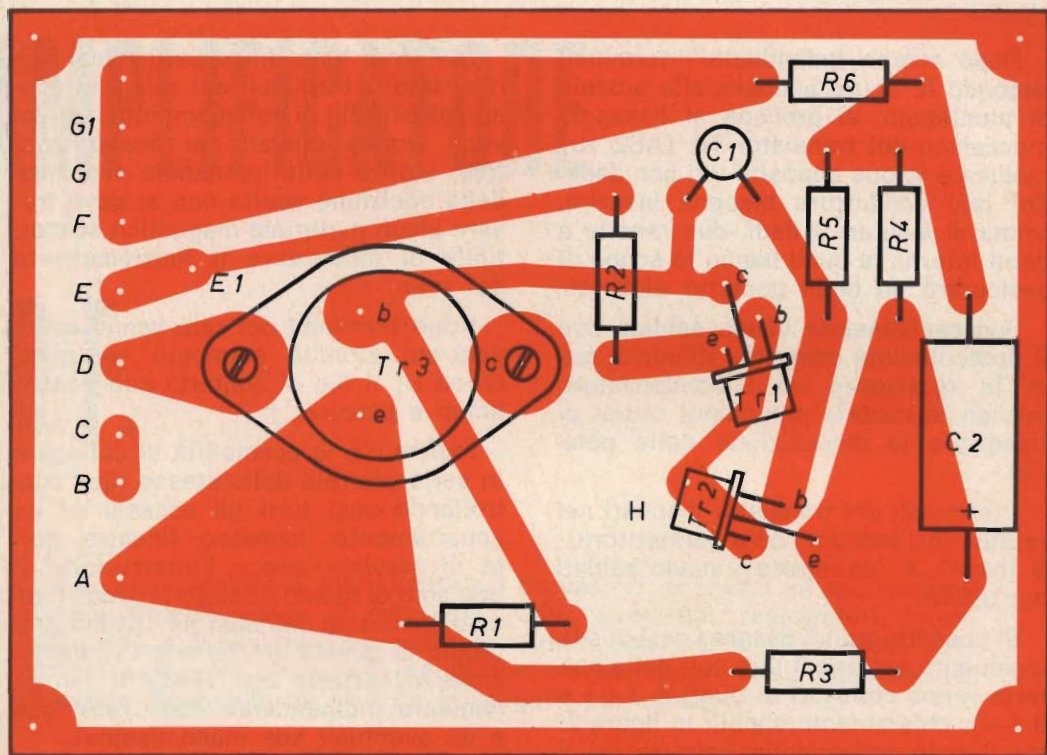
Disposizione dei componenti a montaggio ultimato sulla piastra a circuito stampato.
